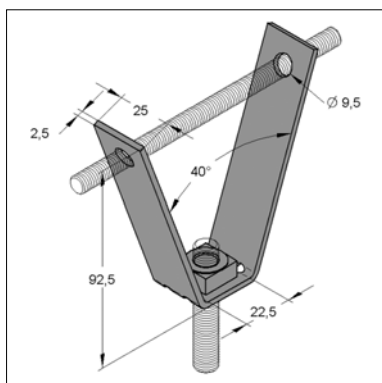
Trapezblechhänger mit eingeschweißter Mutter
